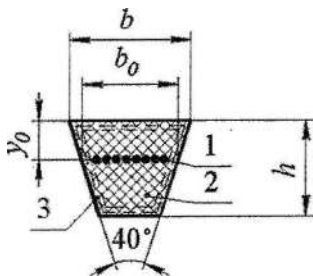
Конструкция и размеры поперечного сечения клинового ремня
